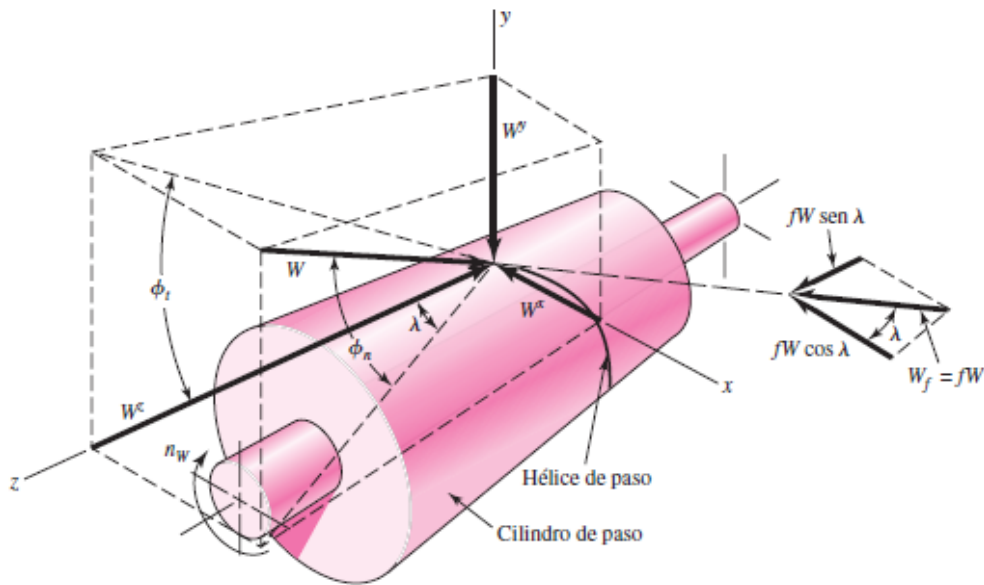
Descomposición de fuerzas en un tornillo sinfín [11]
